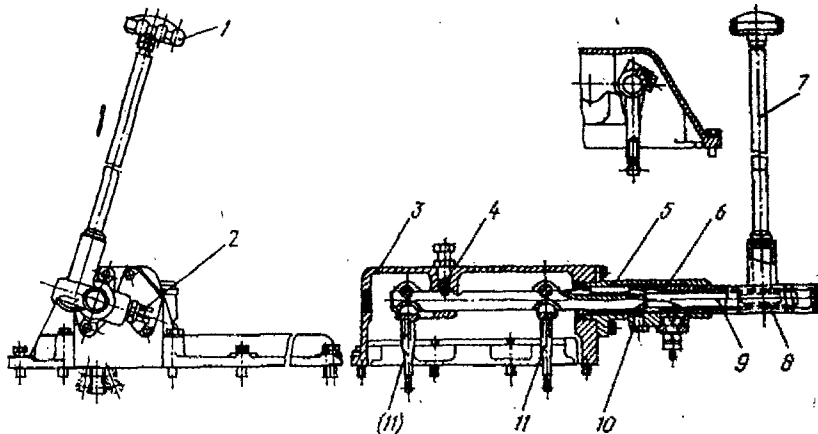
Механизм переключения диапазонов тракторов семейства МТЗ: 1 – рукоятка; 2 – выключатель блокировки запуска двигателя; 3 – крышка; 4 – фиксатор; 5 – кронштейн; 6 – труба; 7 – рычаг с зубчатым венцом; 8, 9 – вал переключения; 10 – стопорный болт; 11 – рычаг
